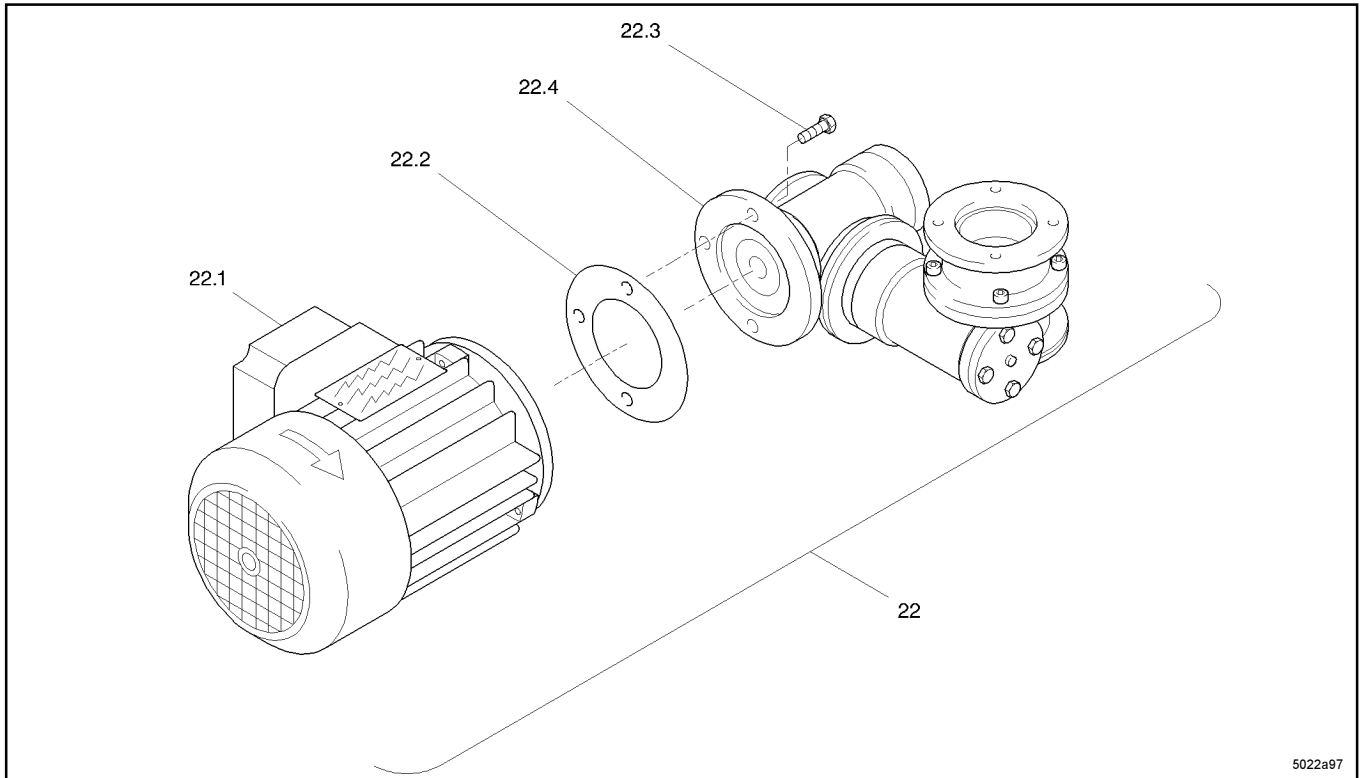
Pièces pour "entraînement avec engrenage double et moteur"
